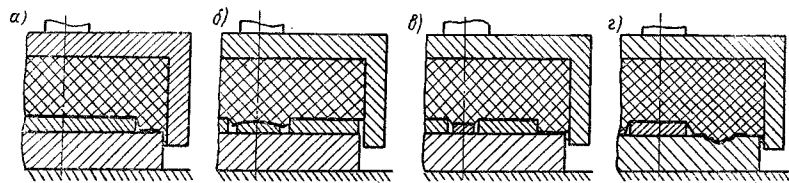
Схемы различных операций вырезки резины: а — вырезка; б — пробивка; в — вырезка и пробивка; г — пробивка и формовка
